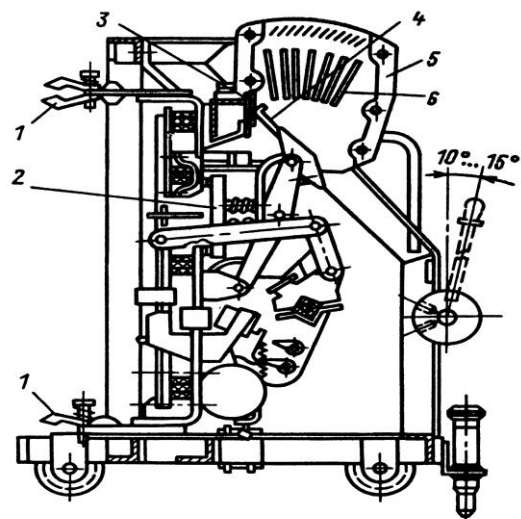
Автоматичний вимикач АВМ: 1 – різні контакти головного кола; 2 - головний рухливий контакт; 3 - нерухомий дугогасильний контакт; 4 - нерухомий дугогасильний контакт; 5 - дугогасильна камера; 6 - сталеві пластини
